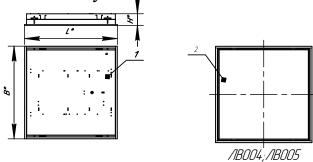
1. Корпус в сборе, 2. Рассеиватель в сборе.
